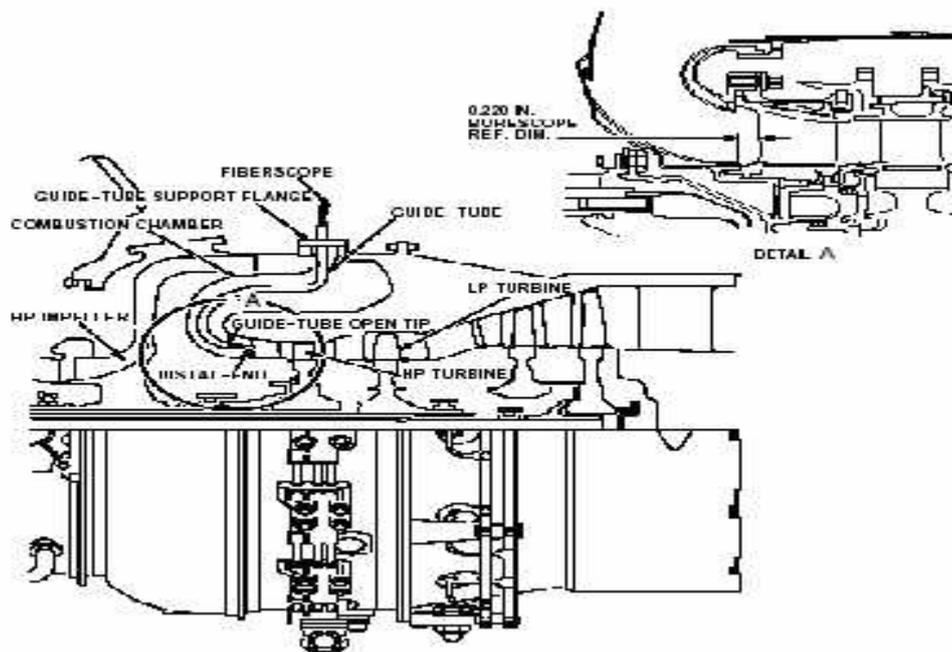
Inspection du stator et des ailettes de la turbine HP.
